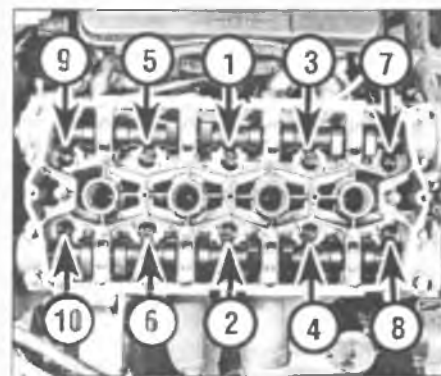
Последовательность затяжки болтов крепления головки цилиндров
